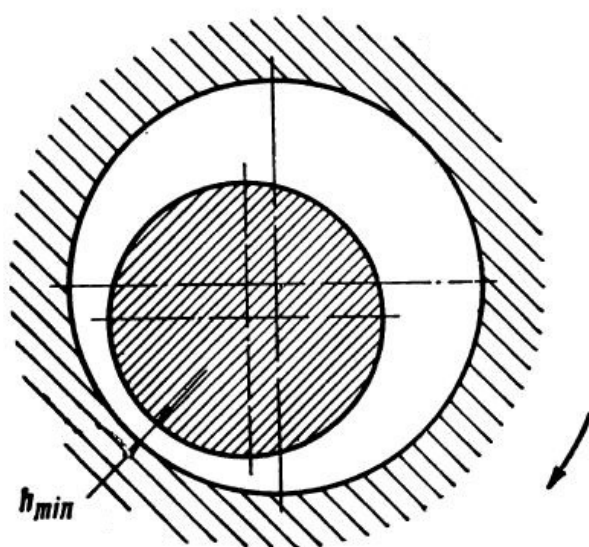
Схема смазки коренных шеек коленчатого вала двигателя
